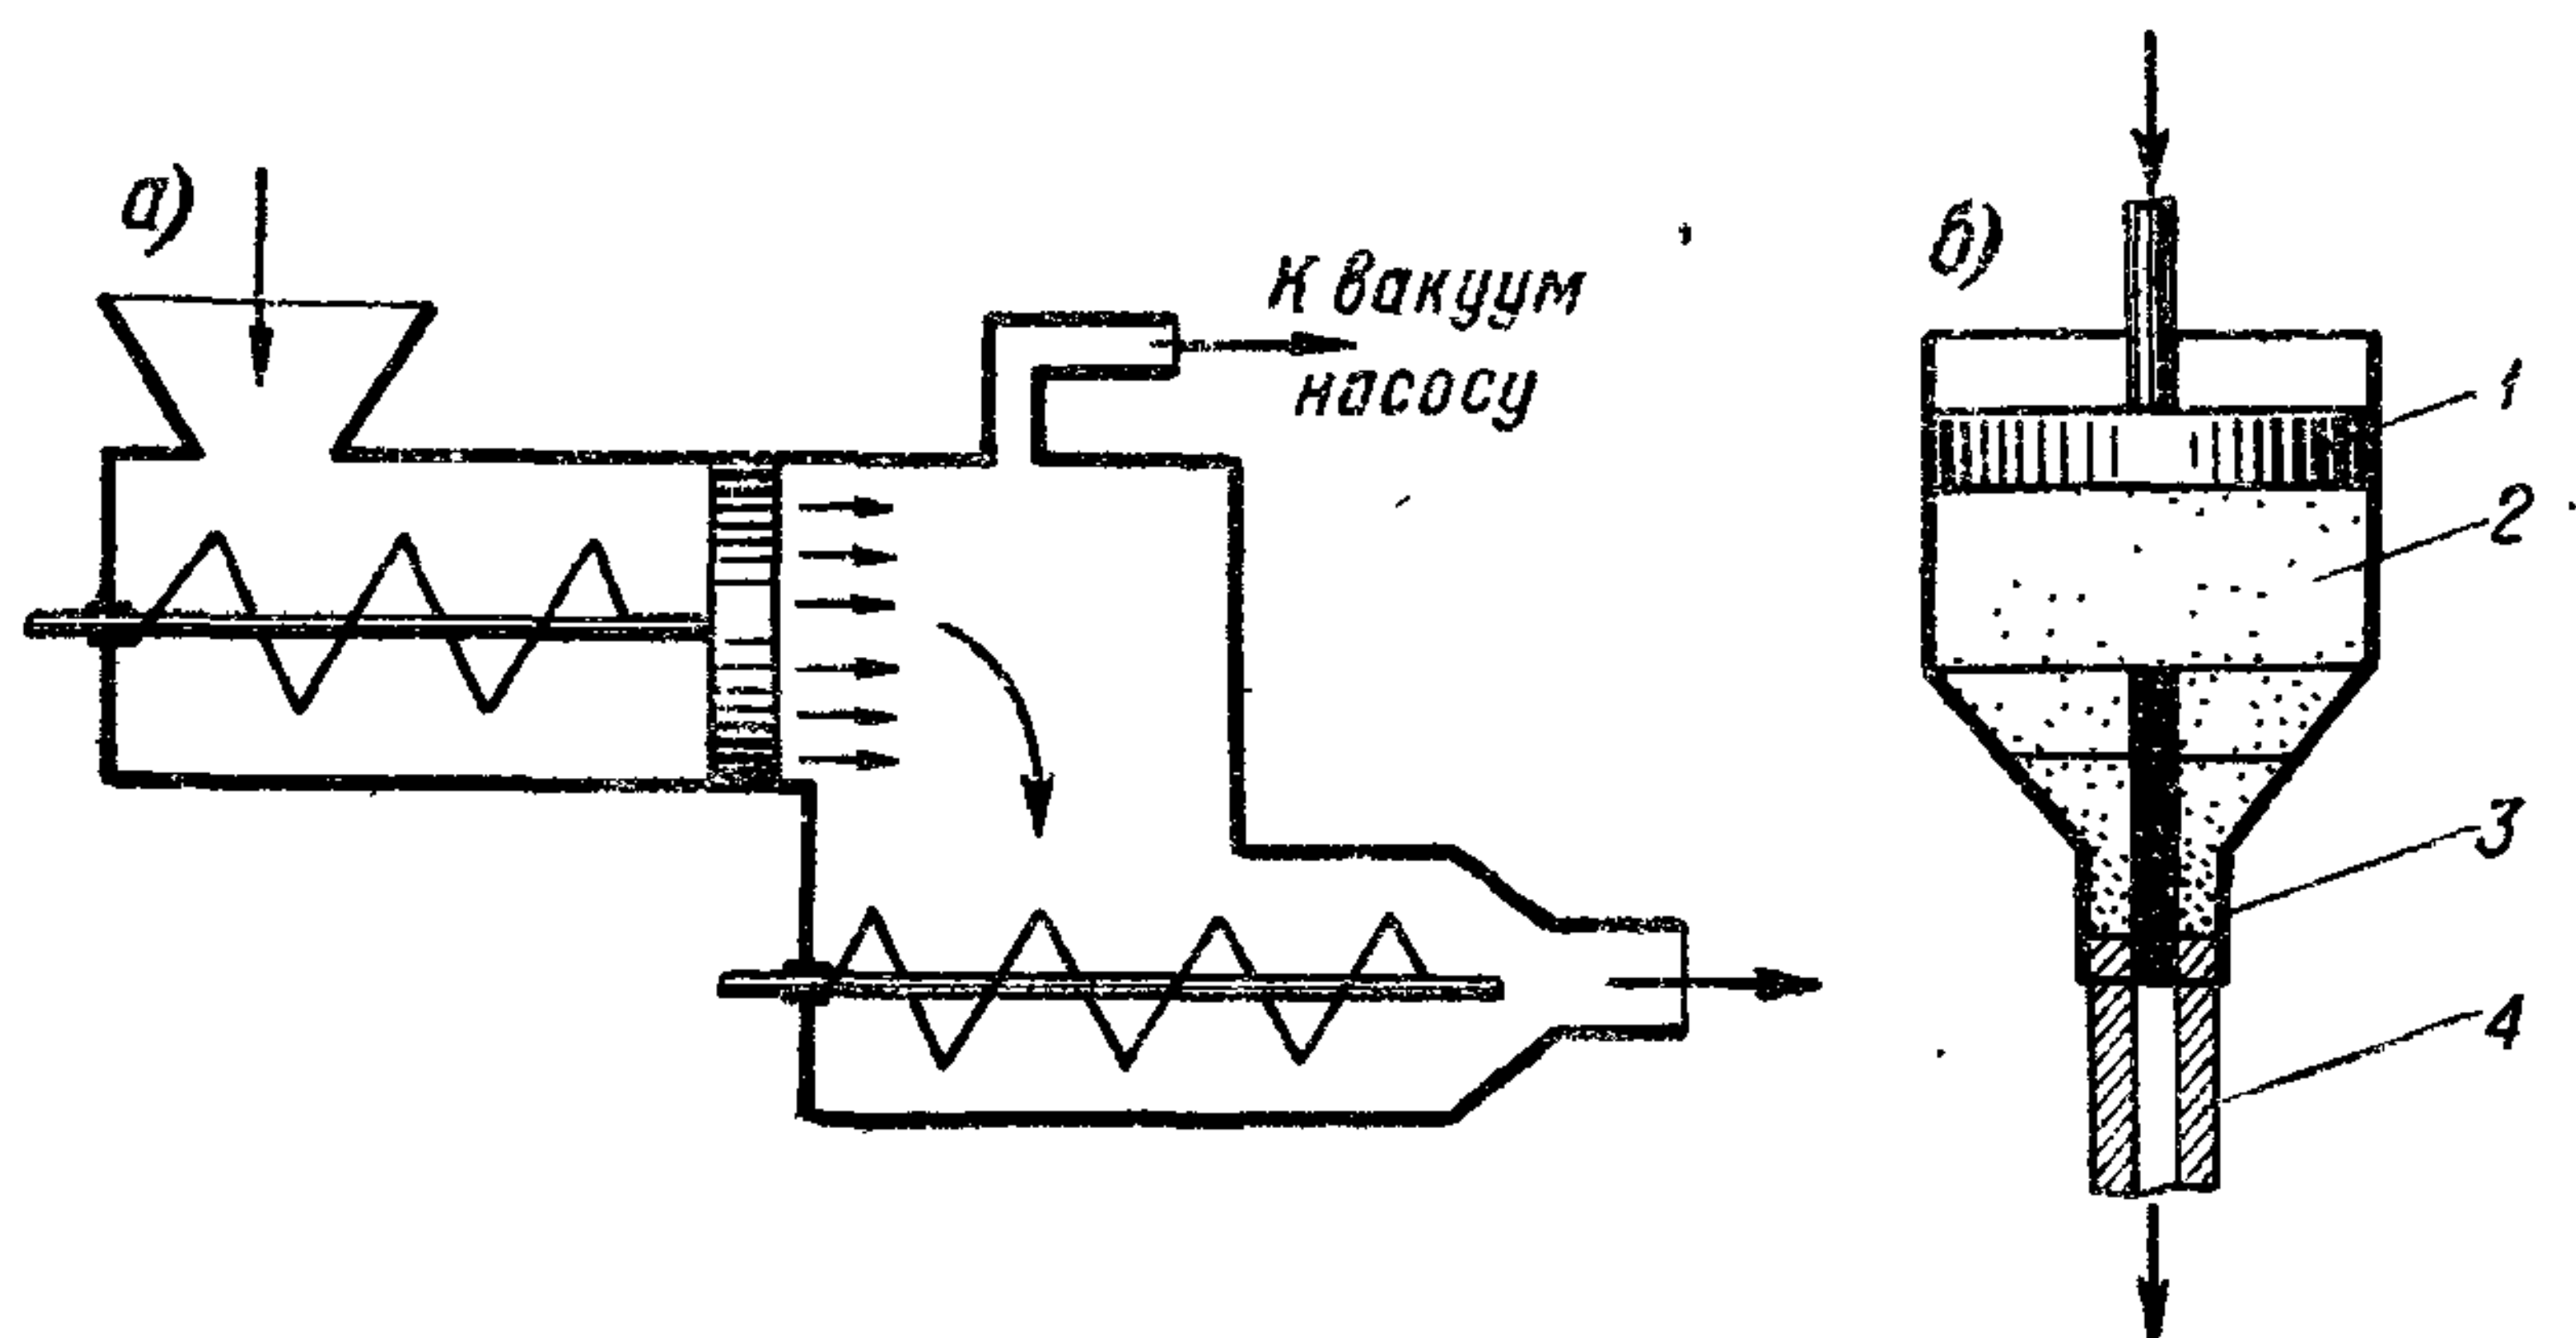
Схема изготовления керамических трубок: а — вакуум-малка для подготовки пластичной массы; б — протяжка (выдавливание) трубки на прессе.
